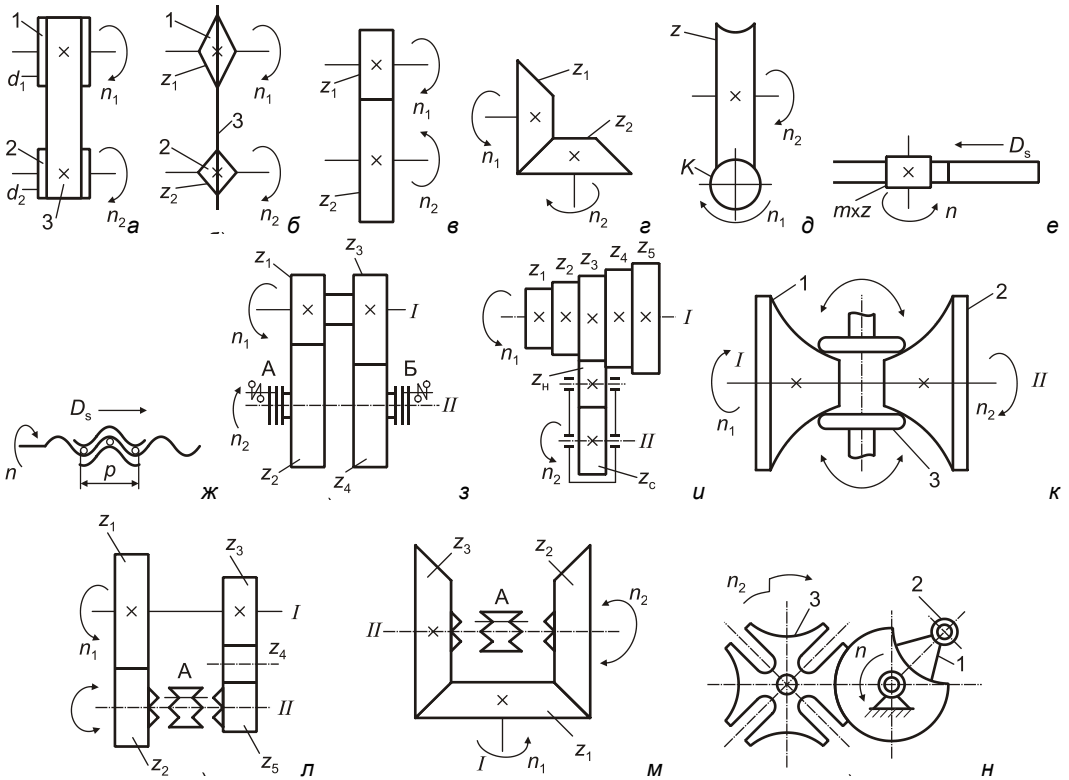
Схематическое изображение передач: а — ременная; б — цепная; в — зубчатая цилиндрическая; г — коническая; д — червячная; е — реечная; ж — "винт- гайка"; з-к — механизмы для изменения скорости; л, м — механизмы для изменения направления; н — механизм для осуществления периодических движений
